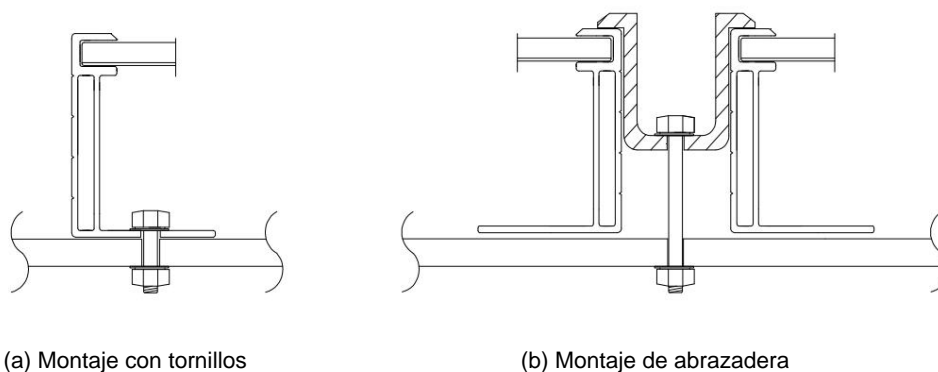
El módulo instalado con (a) montaje con tornillo, (b) montaje con abrazadera
